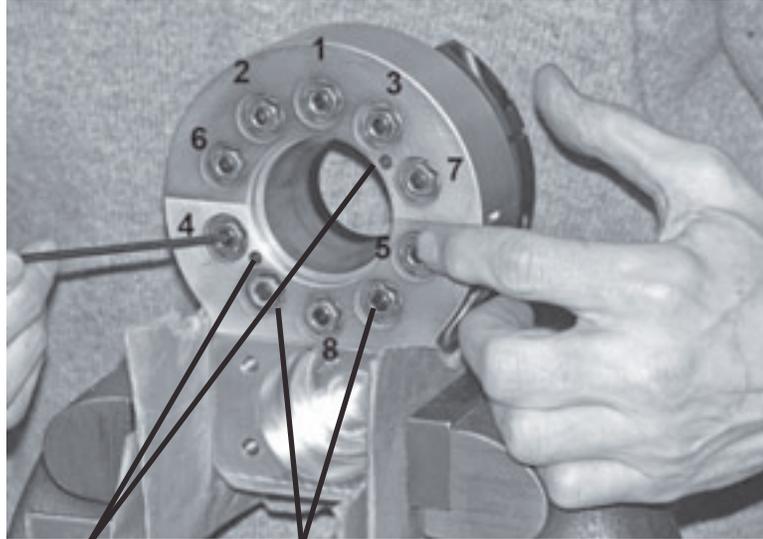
Afloje las tuercas del rodamiento y los ejes de rodamiento como se indica.
